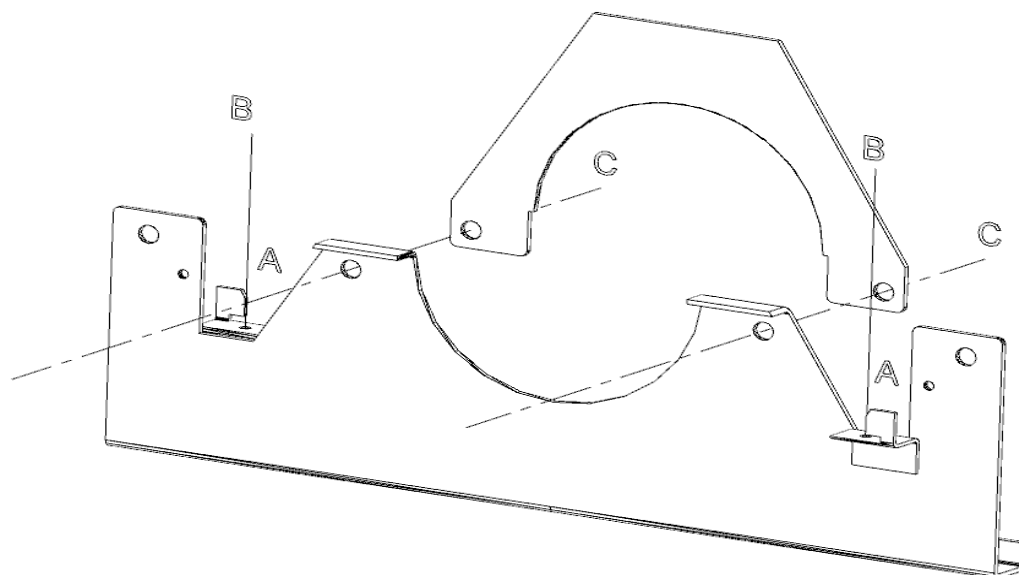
Кронштейн для крепления излучателя SBT в версии "I".
